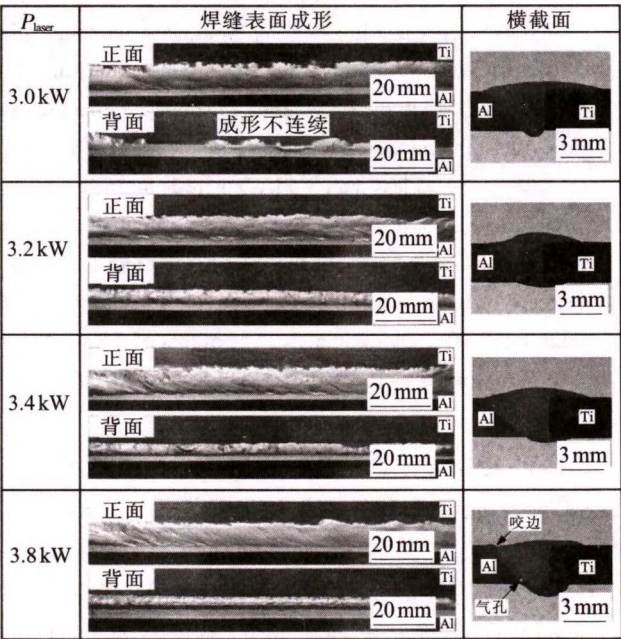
不同激光功率下的焊缝表面成形及横截面形貌
